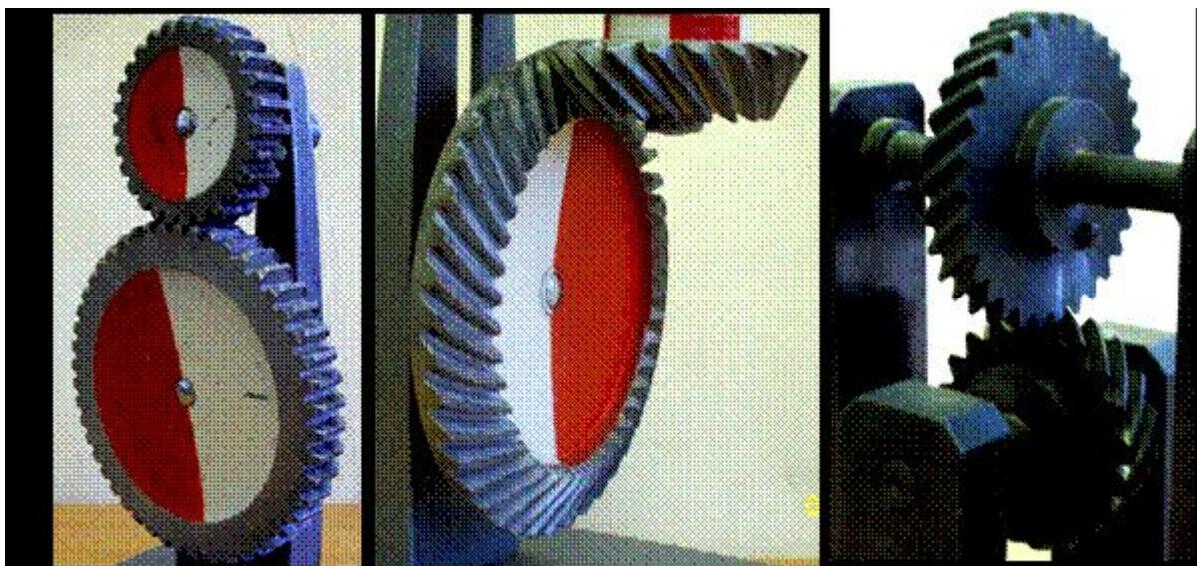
Виды зубчатых передач: цилиндрическая, коническая, винтовая
